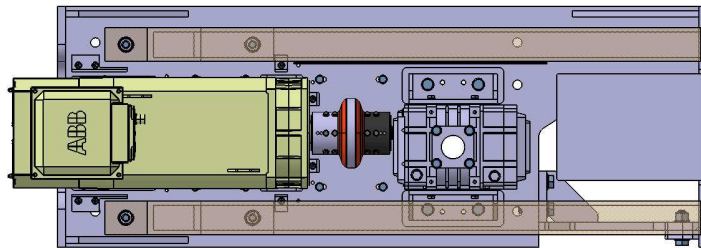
Motor Verdichter Einheit incl. dessen Träger (luftgekühlter Motor)
